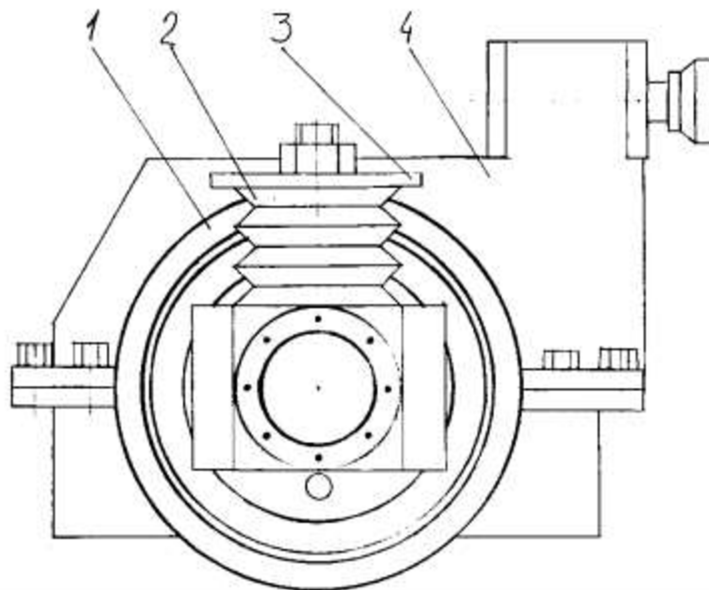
Модернізація приводного колеса зливковоза: 1 – ходове колесо, 2 – пакет тарільчастих пружин, 3 – кришка, 4 – корпус редуктора
